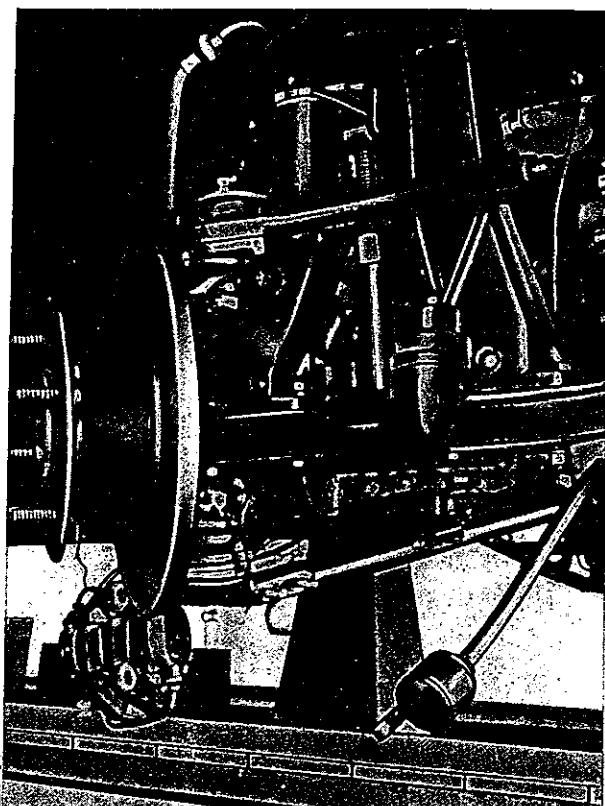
/5 - Mise en place outil 8043111 pour charger le demi-ressort.
